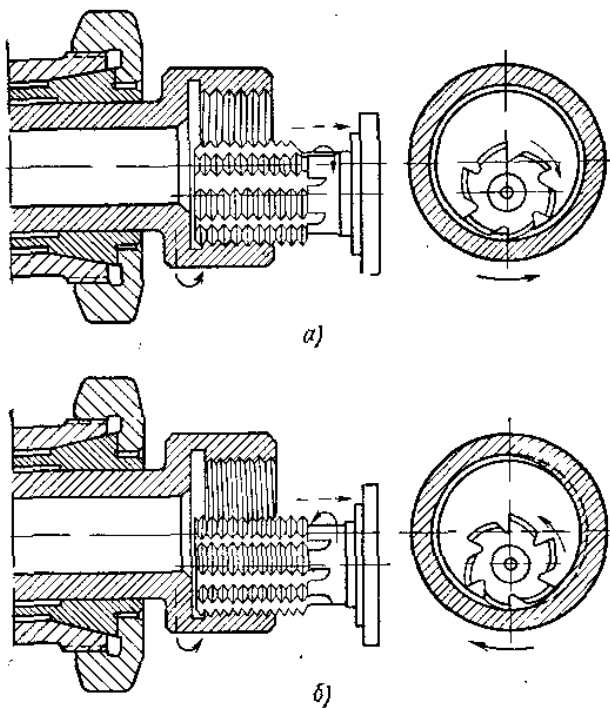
Фрезерование внутренней резьбы гребенчатой фрезой:
